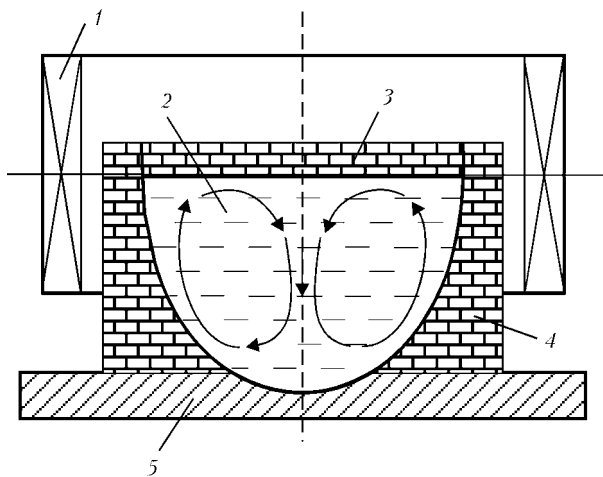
Схема движения макропотоков жидкого металла при обработке изделий: 1 — индуктор; 2 — расплав; 3 — крышка; 4 — тигель; 5 — изделие
